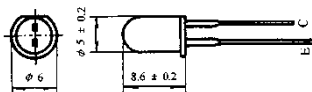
3DU210、220、230 型硅光电三极管外形结构尺寸图
